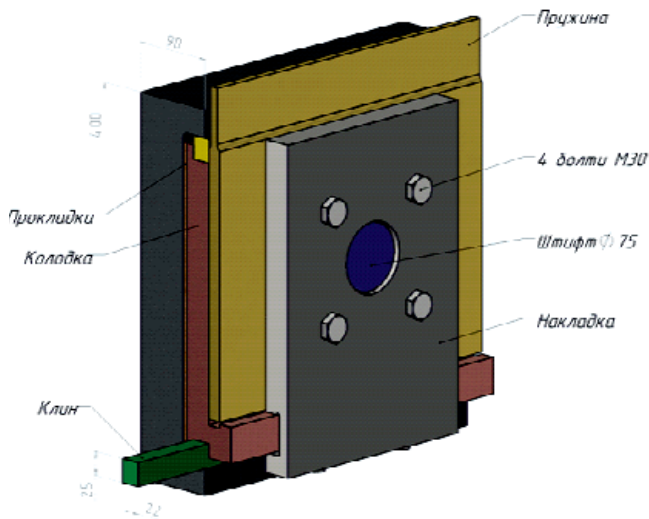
Тривимірне зображення вузла кріплення пружини до корпусу статора.
